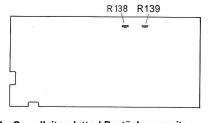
Grundleiterplatte / Bestückungsseite Fig. 1 Basic circuit board / Components side Fig. 1 Plaquette imprimée du cäblage
